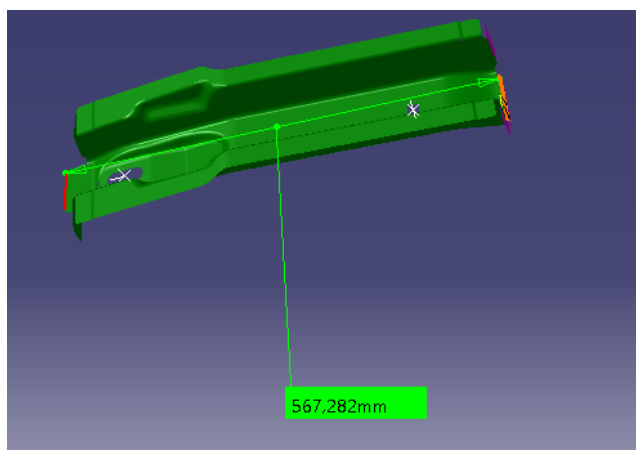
dimension du Longeron AV G-D (Réf : 751338894R)
